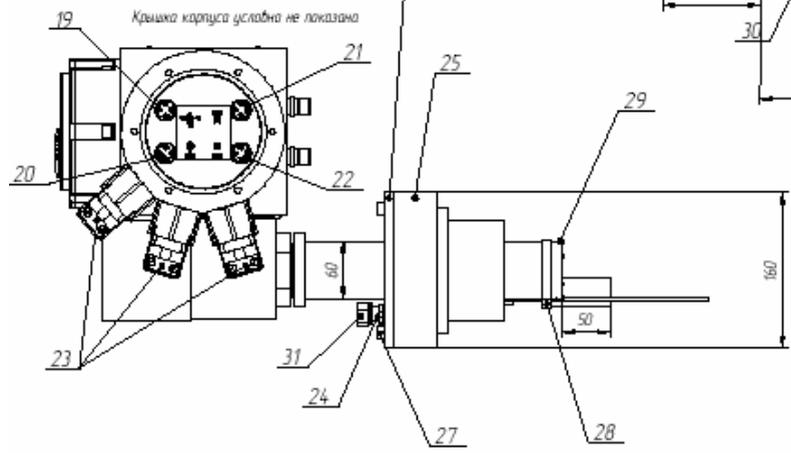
Внешний вид газоанализаторов АКВТ-02 с разметкой для монтажа
